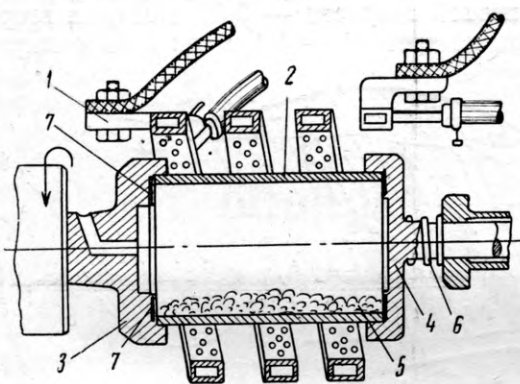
Схема закрепления вкладыша или втулки для заливки:
